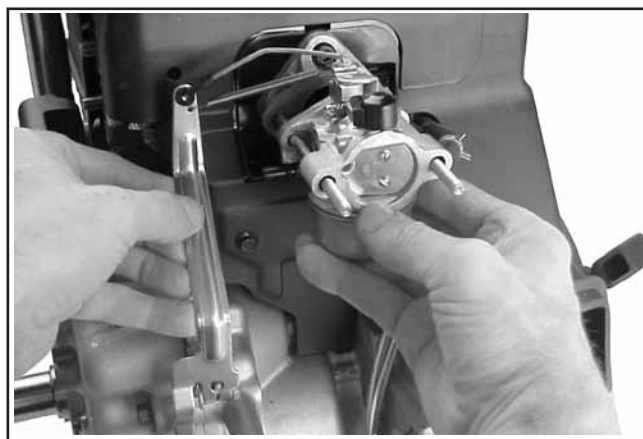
Installation du carburateur et des composants externes du régulateur.
